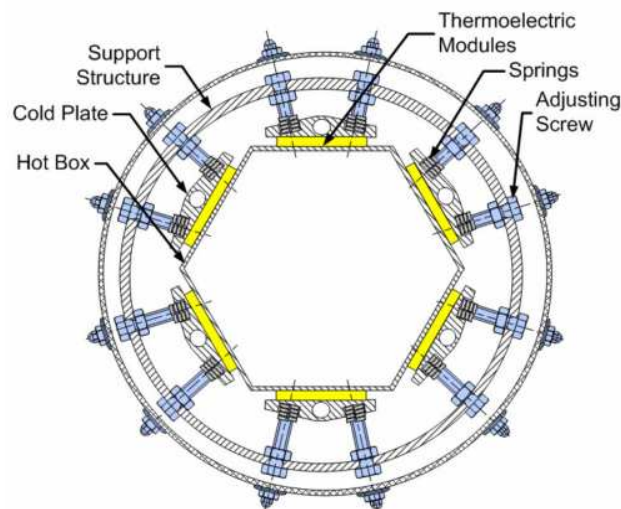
Termoelektrický generátor testovaný Univerzitou v Karlsruhe [34]
